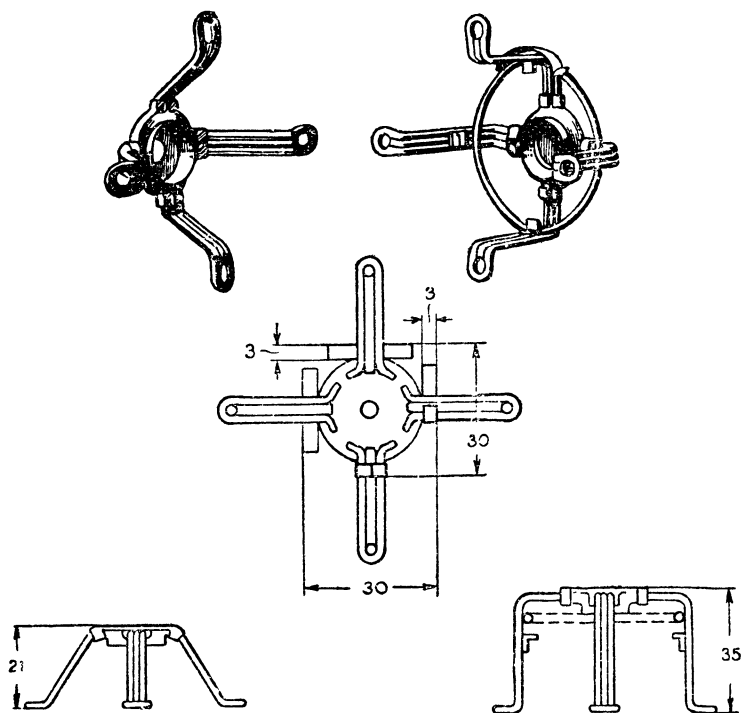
Передняя (слева) и задняя крышки двигателя. В центре — крестовина.
